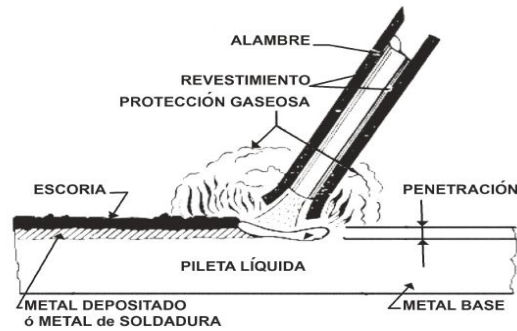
Proceso de Soldadura -SMAW , (ESAB ,2020)
